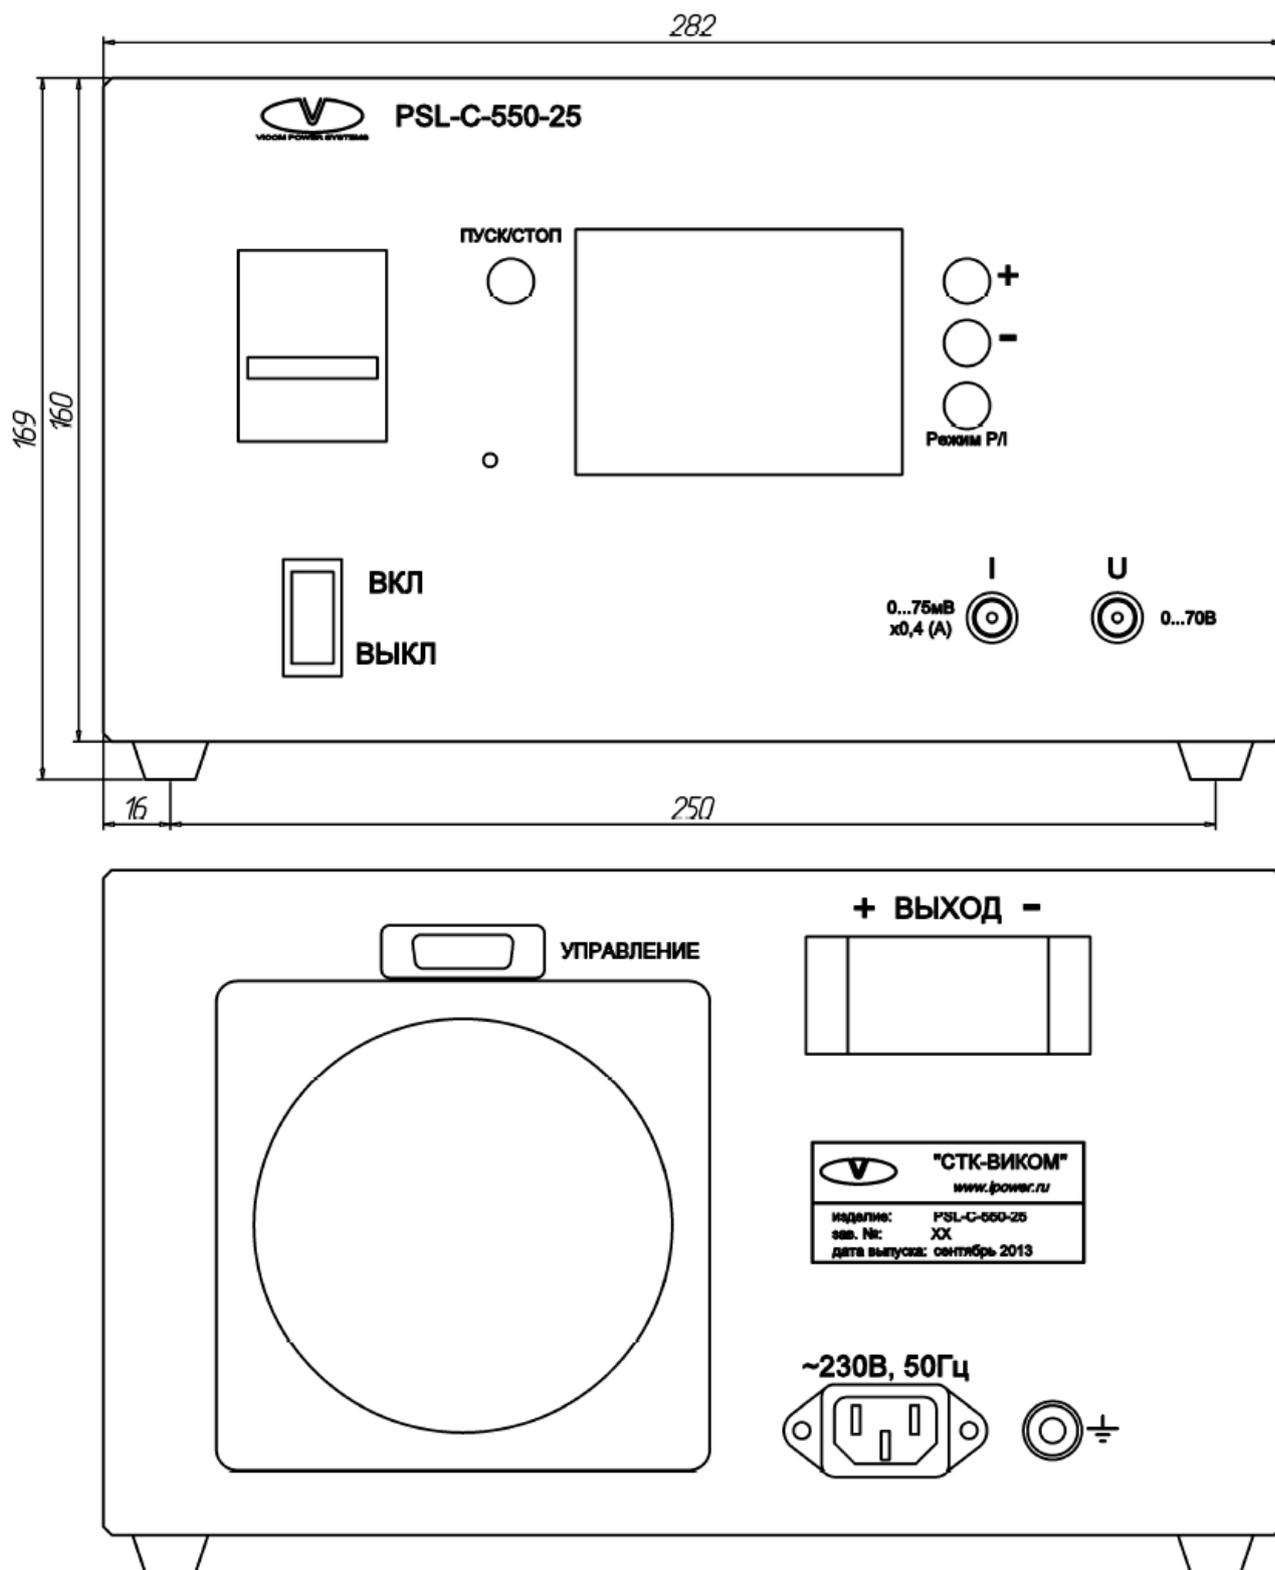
Габаритные размеры ИП. Вид спереди и сзади.
